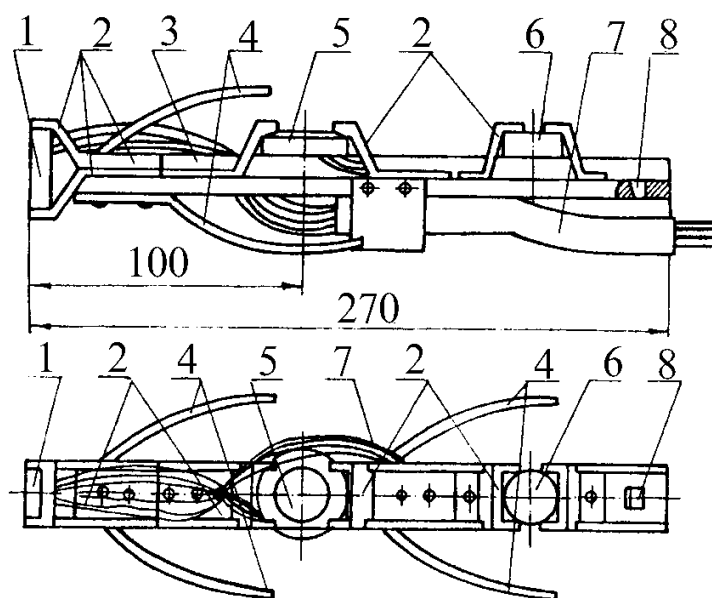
Конструктивная схема измерительного модуля первого типа: 1,5,6 - датчики; 2 - детали крепления датчиков; 3 - корпус измерительного модуля; 4 - центрирующие элементы; 7 - провода; 8 - гнездо для зацепа головки захвата узла доставки модуля в шпур
